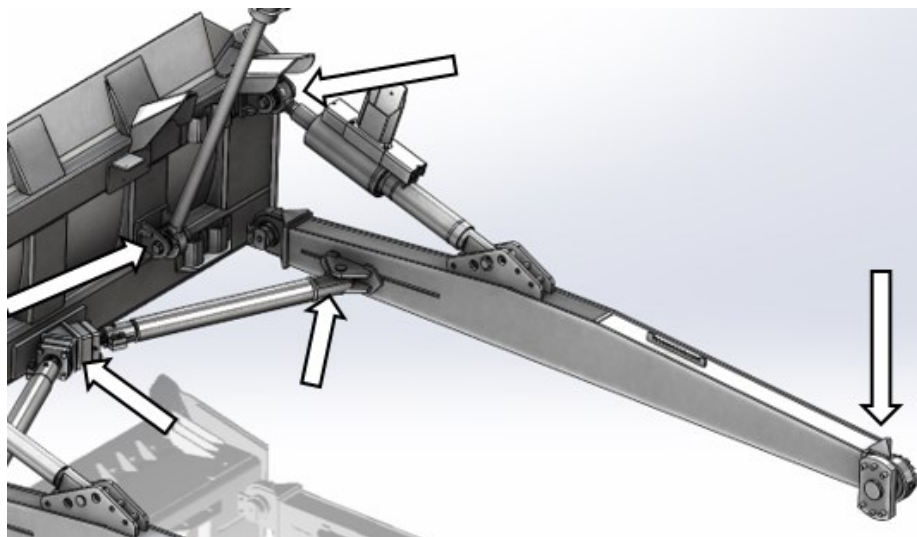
Точки смазки бульдозерного отвала со съемными брусьями (точки смазки показаны стрелками)
